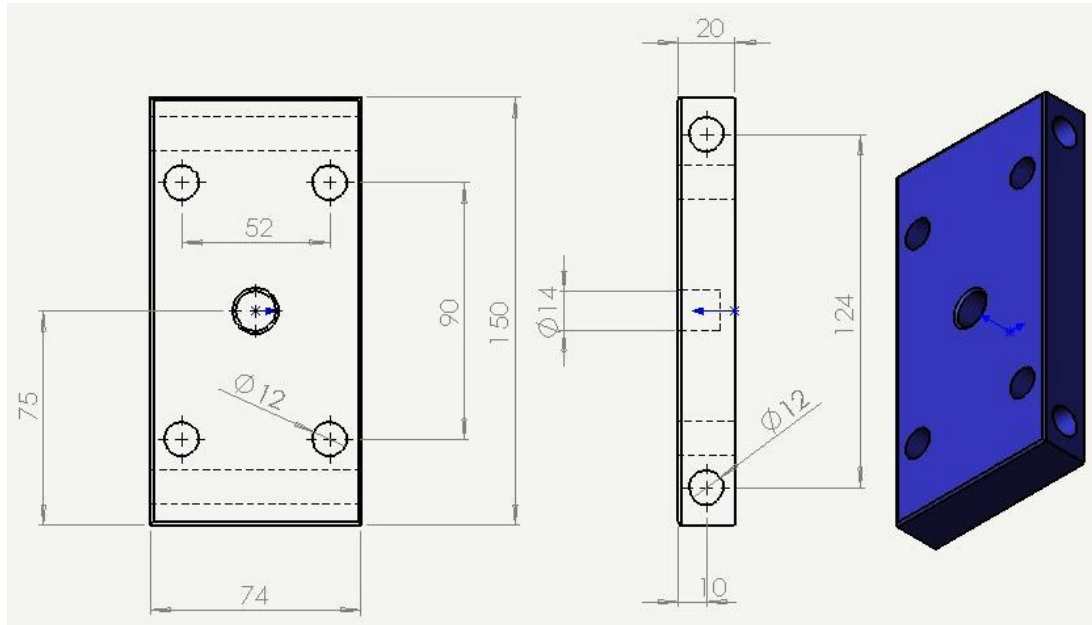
Dimensiones expresadas en milímetros y figura en 3D de la placa de sujeción de la tuerca, referente al Eje Y
